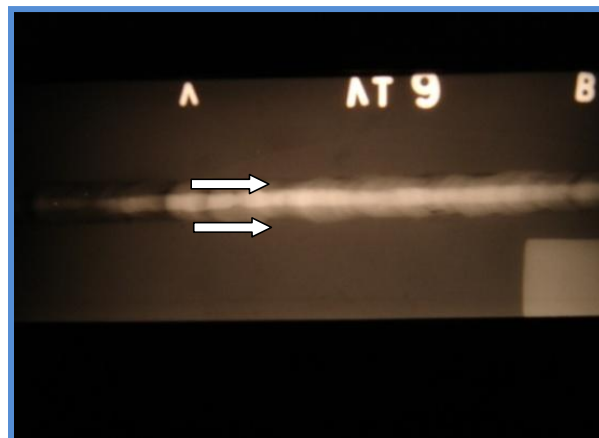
, Probeta N° 09: Falta de Fusión.
